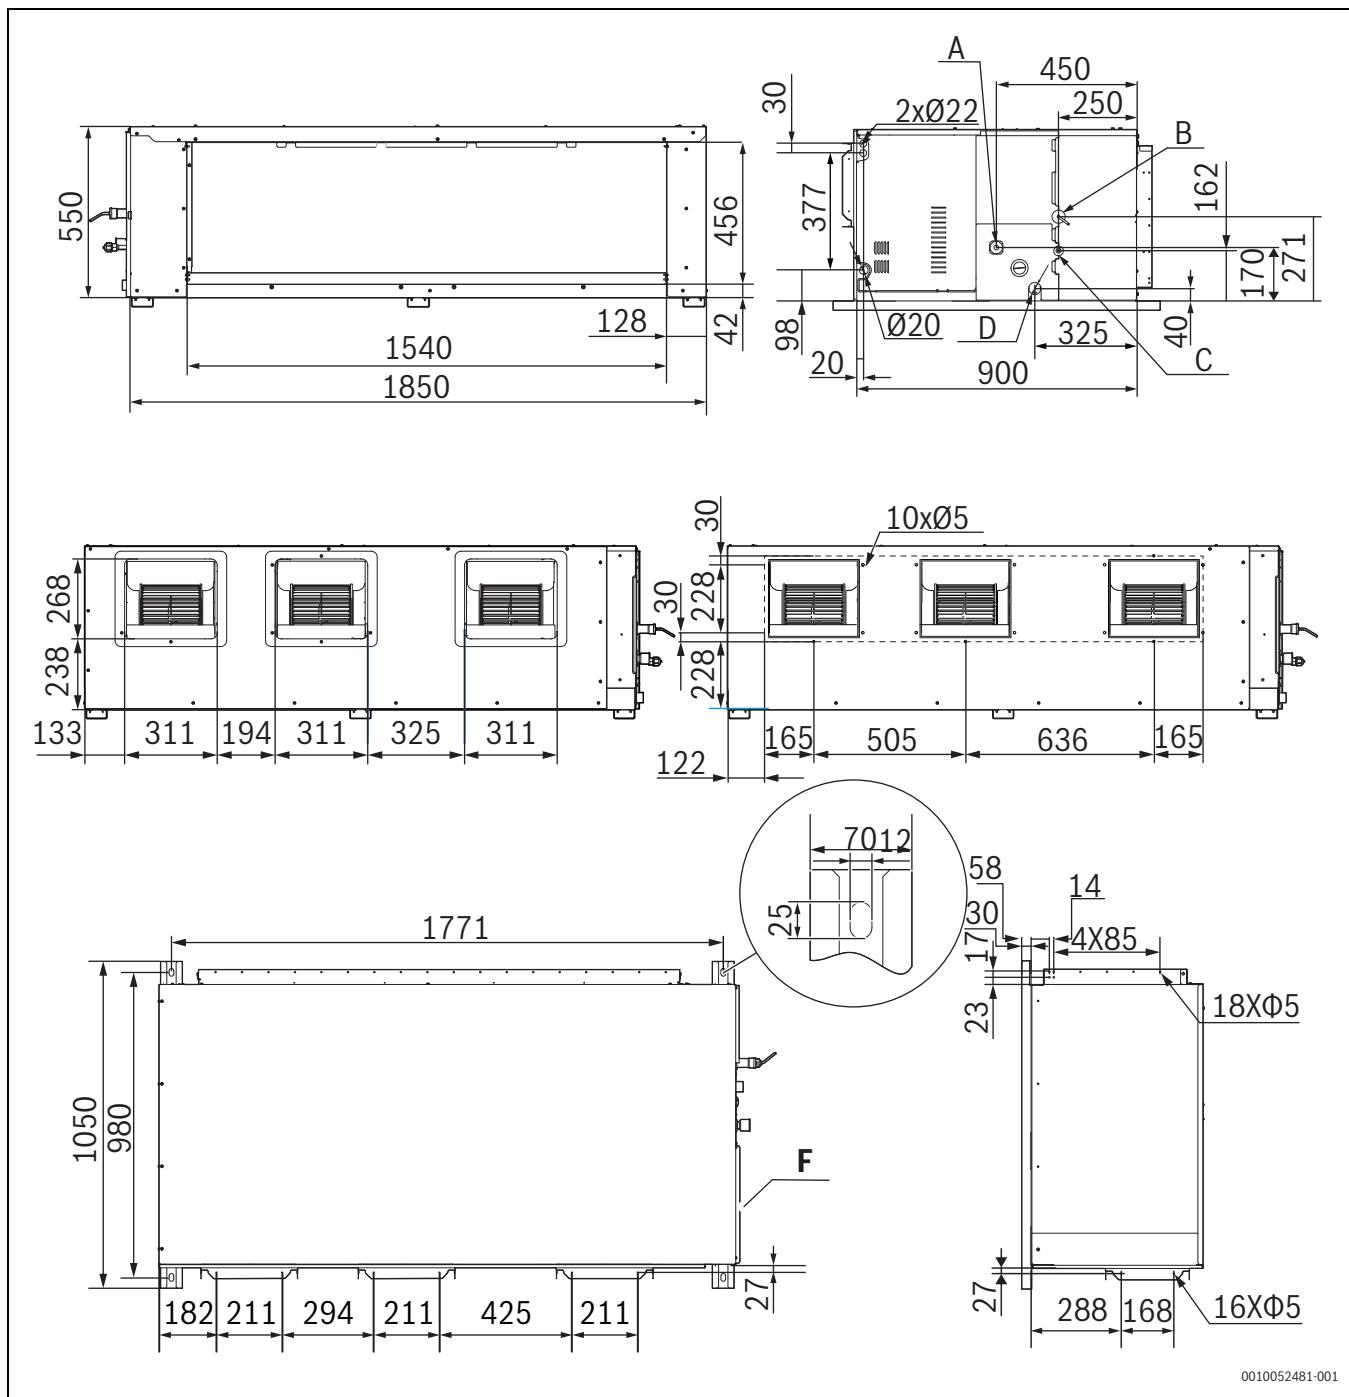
Dimensions extérieures et taille de la bride de soufflage (AF2-DH 200-1 – AF2-DH 335-1) (unité : mm)
